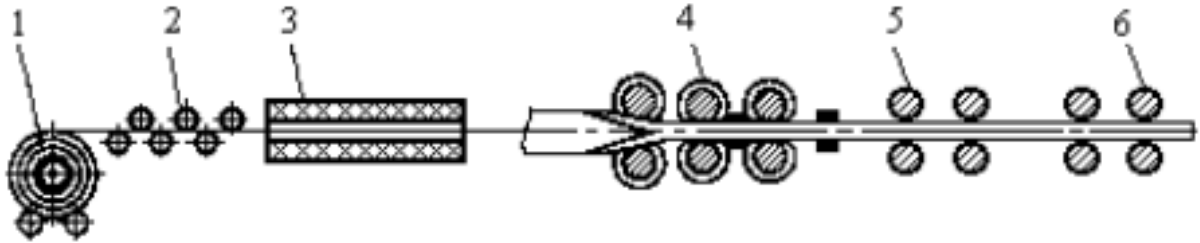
Схема пічного зварювання труб: 1 - рулон заготовки, 2 - правильна машина, 3 - нагрівальна піч, 4 - формовочно-зварювальний стан 5,6- обтискні кліті
